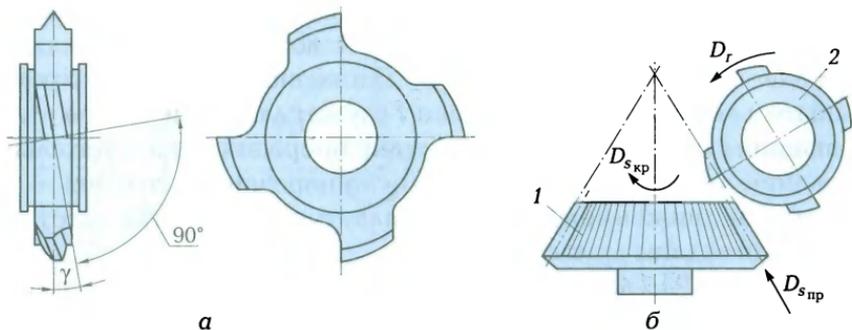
Нарезание конических зубчатых колес специальной дисковой фрезой с винтовыми зубьями:
